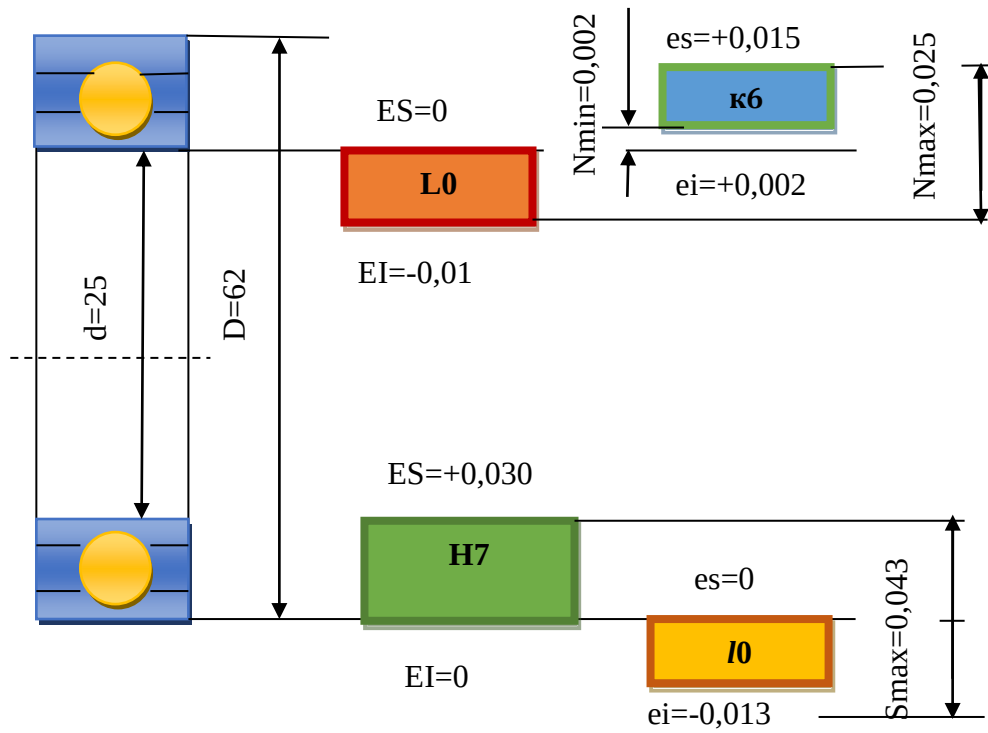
Схема расположения полей допусков для соединений с подшипником качения
